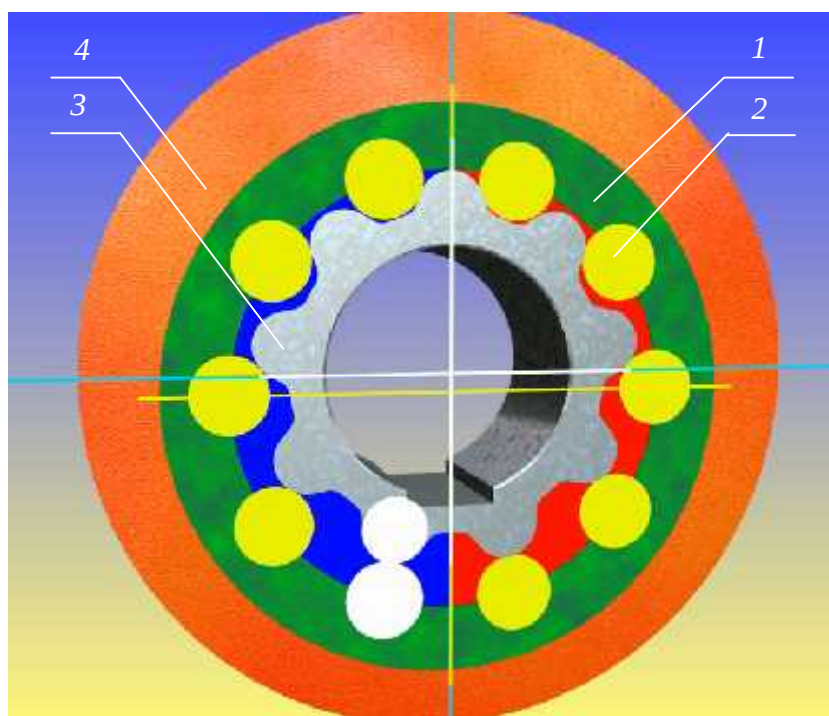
Компенсирование героторного движения вытеснителей с помощью смещения вытеснителей (роторов): 1 – охватывающий вытеснитель; 2 – ролики; 3 – охватываемый вытеснитель; 4 – корпус.
